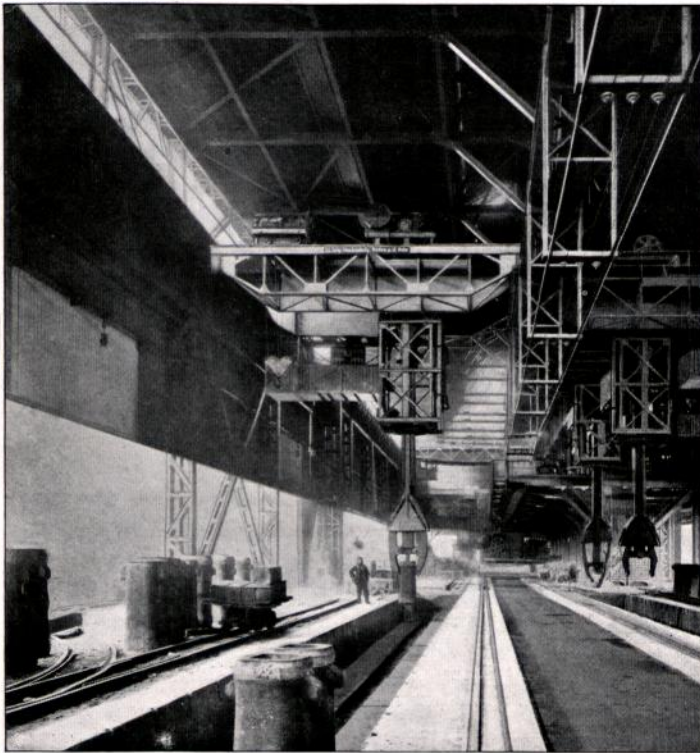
Gießhalle eines Stahlwerks mit Stripperkranen.
